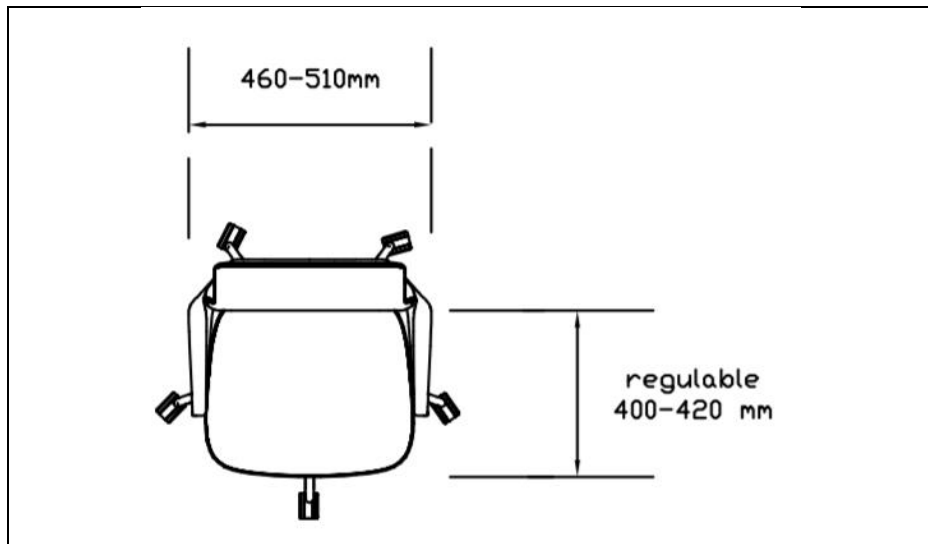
Vista superior, dimensiones profundidad del asiento
